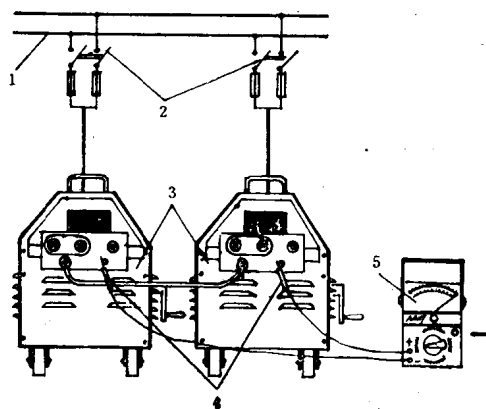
交流弧焊机并联使用接线的检查方法
